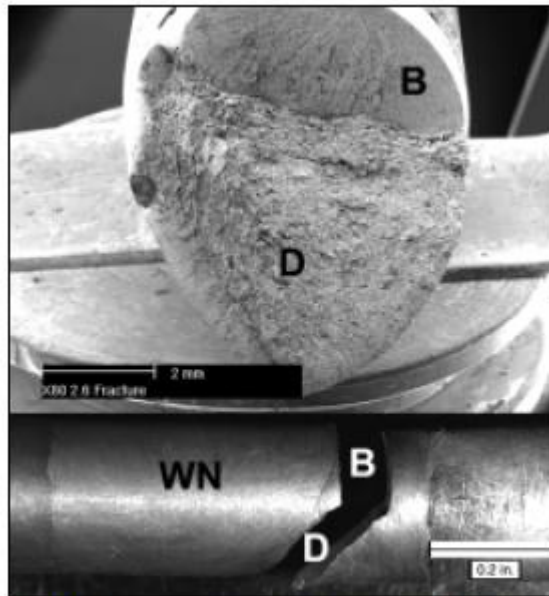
Muestra la Morfología de la fractura completa (b) fractura frágil, (d) fractura dúctil en un acero API X70.
